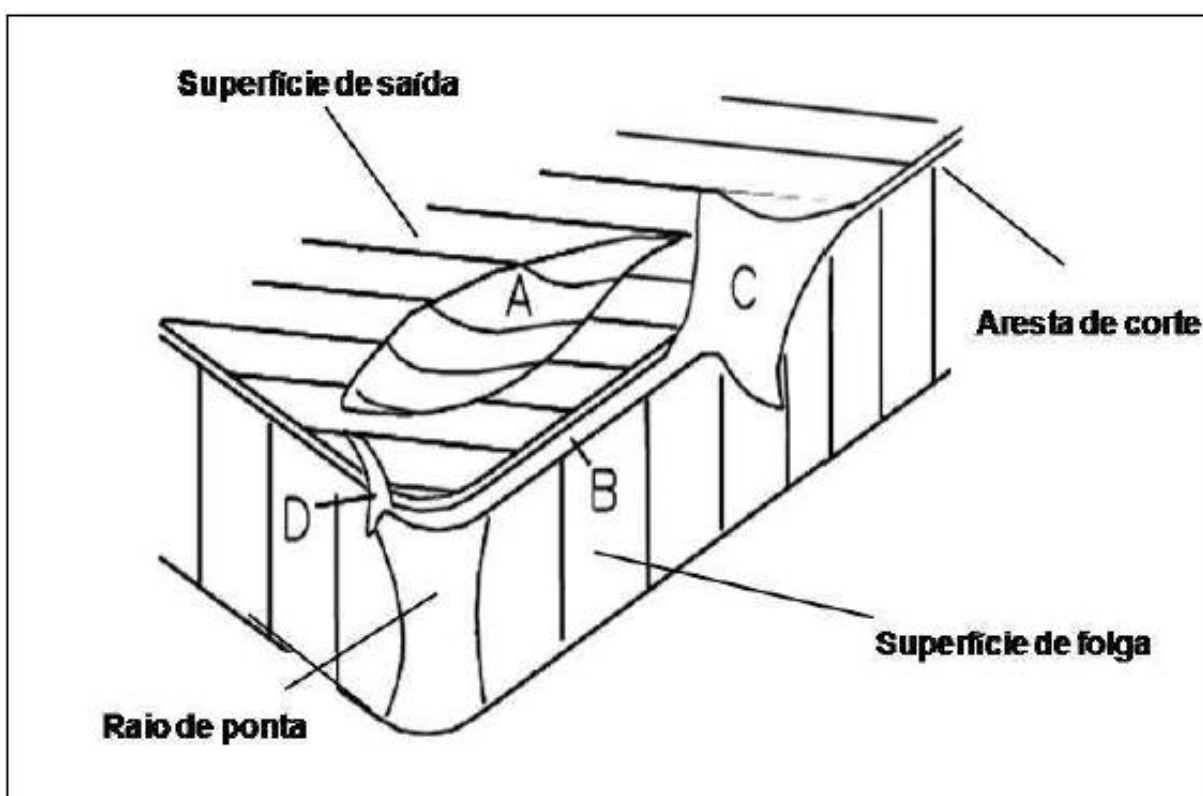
Avarias e desgastes que ocorrem em ferramenta de corte: (a) cratera, (b) flanco e (c,d) entalhe
